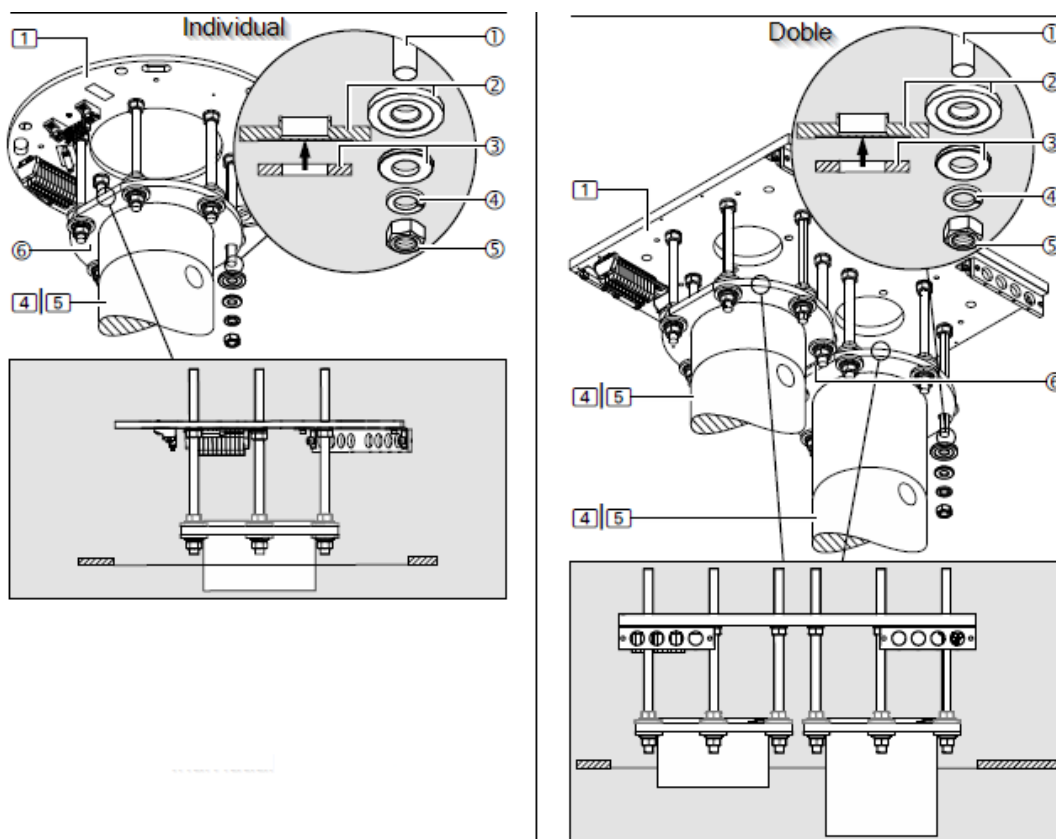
Assemblage de la bride du tube de toit sur les boulons filetés
